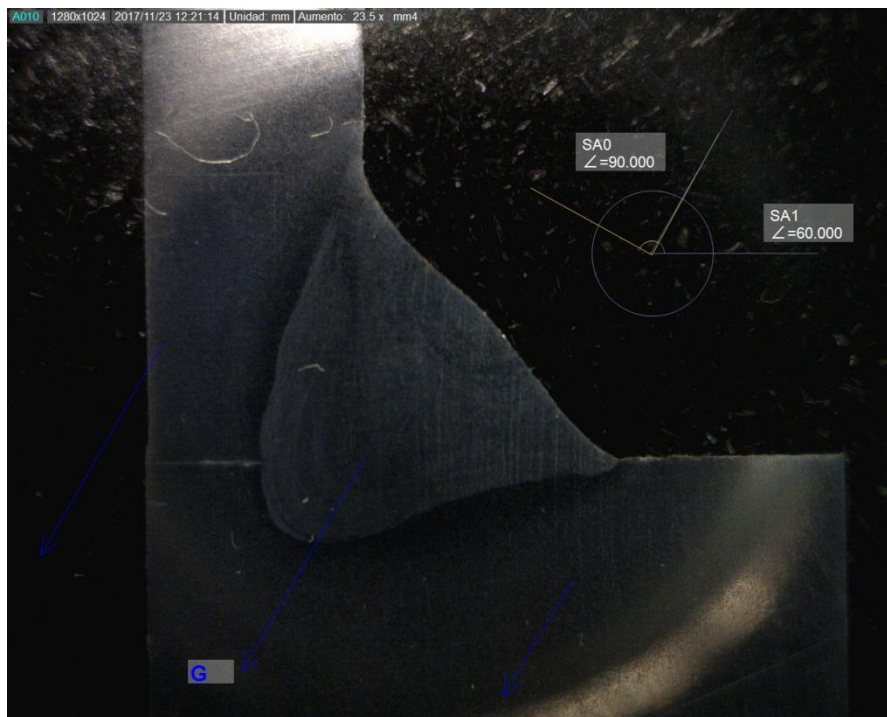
4 Perfil obtenido en cupón de soldadura 2B.
